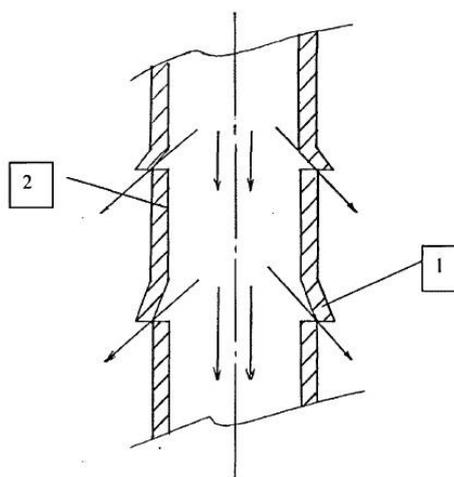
Схема полого вала с жалюзийными отверстиями для выхода воздуха в питательную смесь
